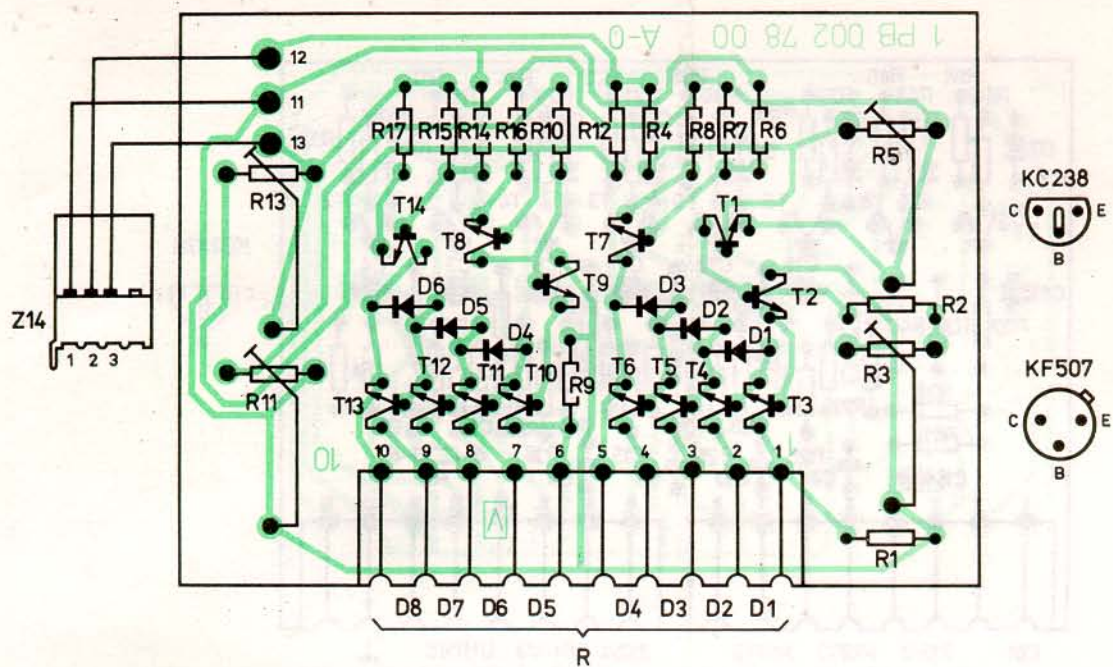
Montážní zapojení mikrospínačů a indikátorů (R)
